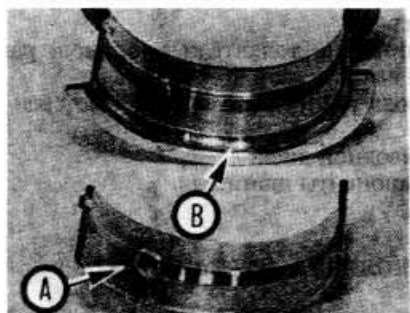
Вкладыш коренного подшипника (А) и вкладыш среднего коренного подшипника (В) с упорным фланцем
